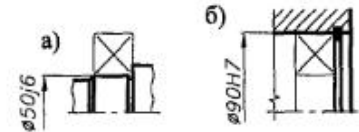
Обозначение посадок мест под подшипники: а) на валу; б) в отверстии корпуса
